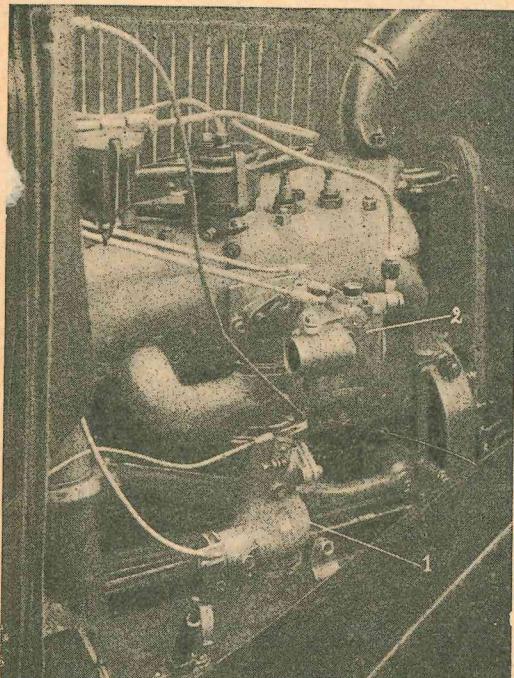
Монтаж смесителя и карбюратора Солекс на двигателе ГАЗ, приспособленных для работы на газе (смеситель старой конструкции): 1—смеситель; 2—карбюратор
